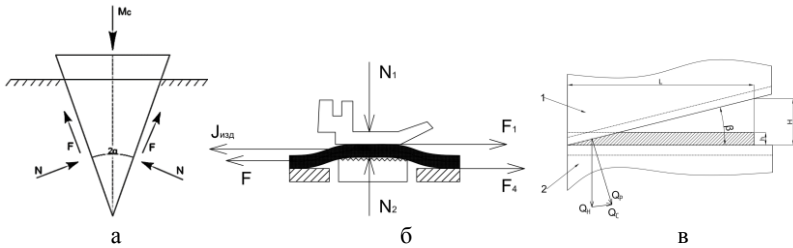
Схема сил полезного сопротивления иглы (а), зубчатой рейки (б) и верхнего ножа (в)
